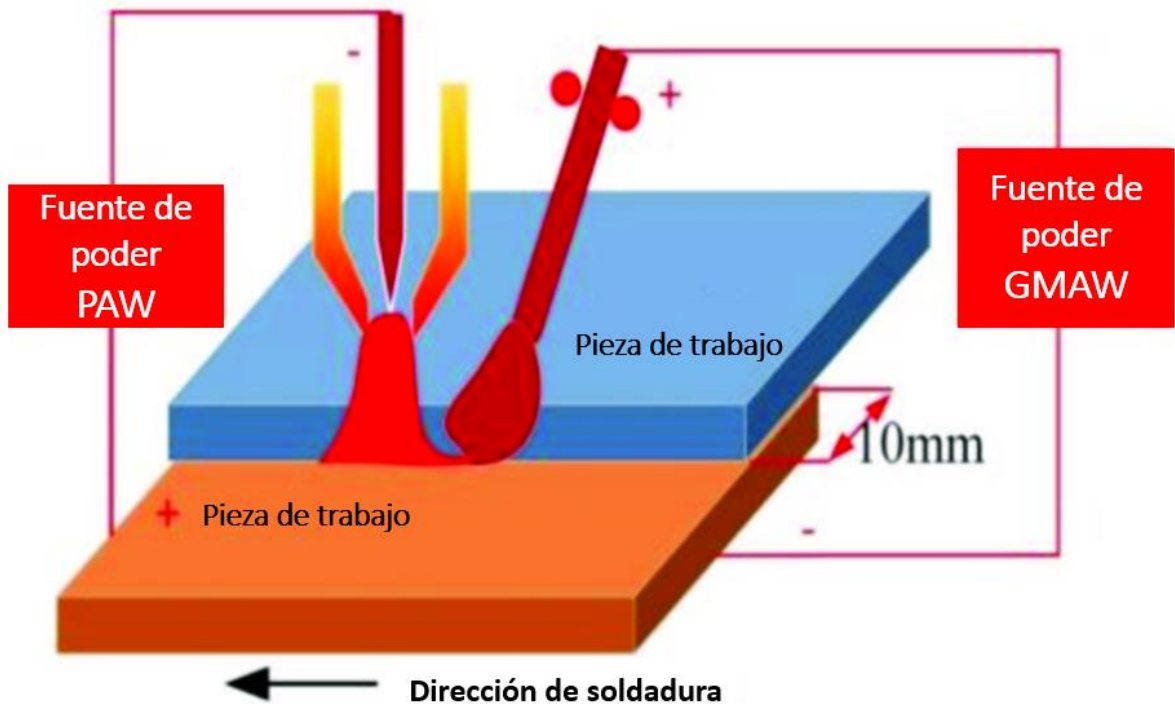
Proceso de soldadura híbrida PAW-GMAW. (Modificado de Zhang y col. (2023))
